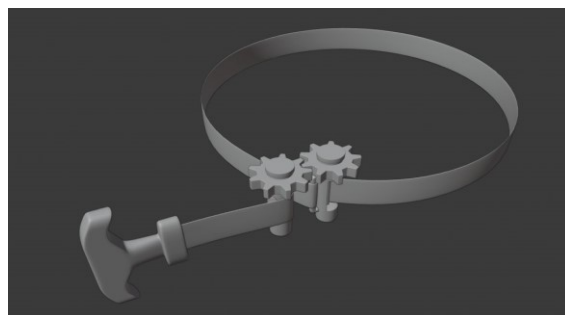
Концепт крепёжного стягивающего механизма без корпуса
